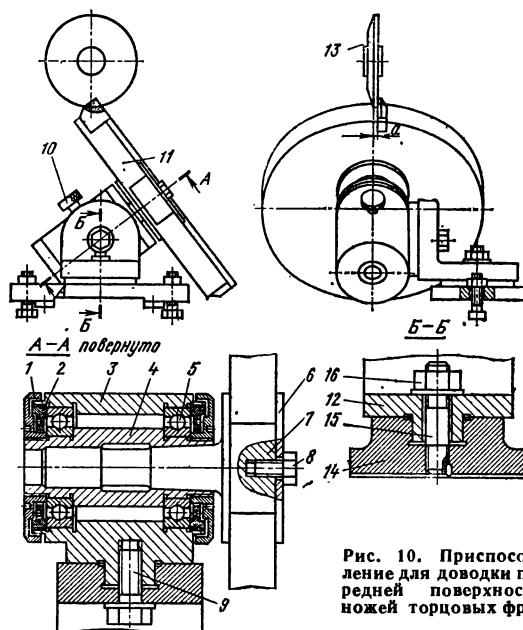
Приспособление для доводки передней поверхности ножей торцовых фрез
